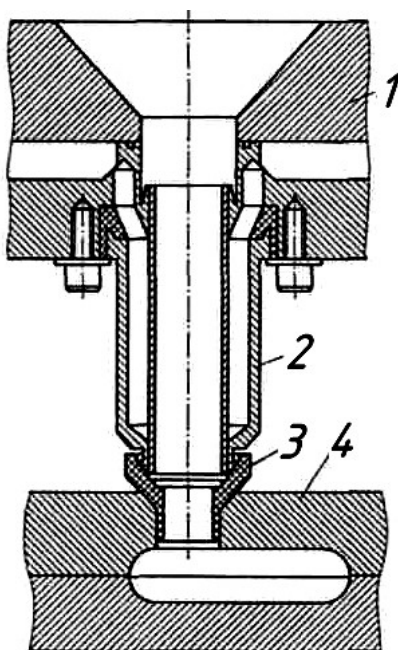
Надувные плиты с металлическими водоохлаждаемыми соплами: 1 – надувная плита; 2 – водоохлаждаемое сопло; 3 – резиновый наконечник; 4 – стержневой ящик
